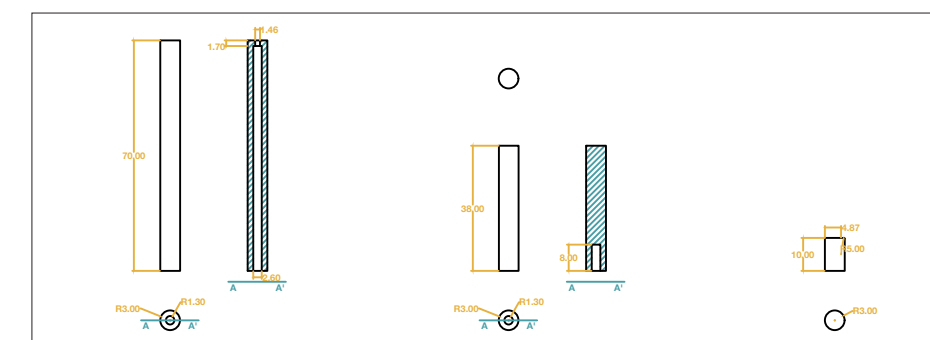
Planta, alzado y sección de la Columna Mesa, de la Columna Banco y del Tapón.
